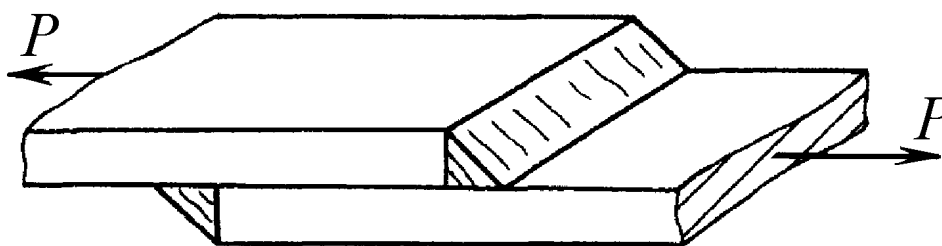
Схема среза швов в сварном соединении
